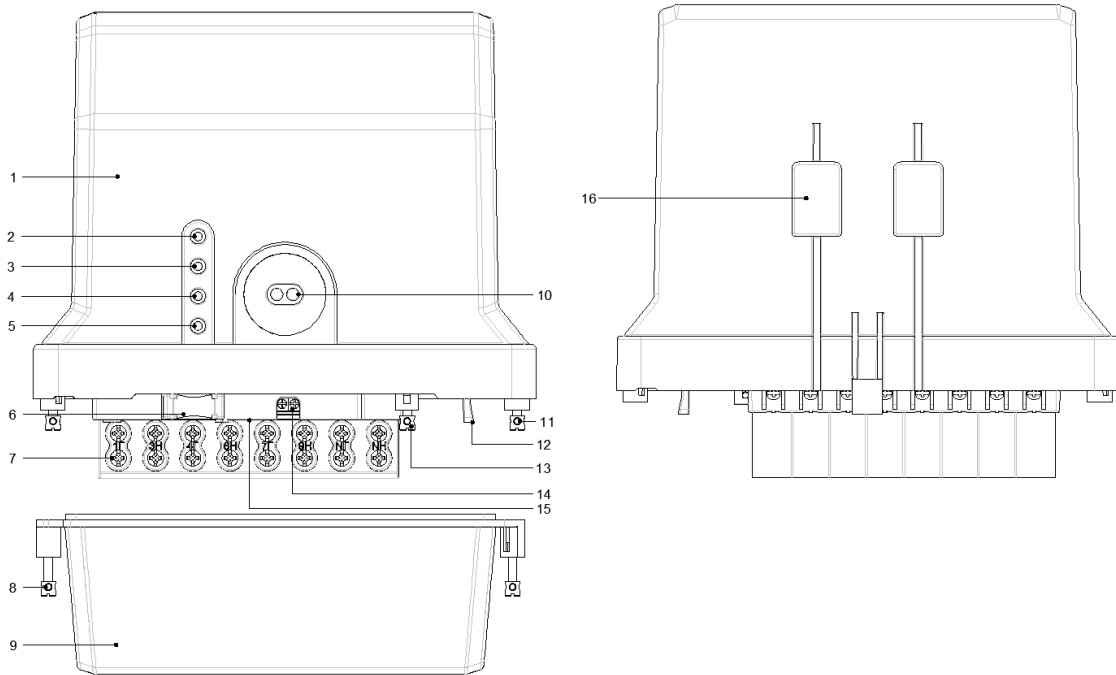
Габаритный чертеж счетчика в корпусе W135
